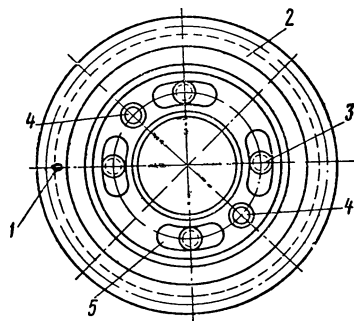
Схема размещения контрольных штифтов, шпилек и контрольной метки на шестерне кулачкового вала топливных насосов: 1 — контрольная метка 0; 2 — шестерня; 3 — шпилька; 4 — отверстия для контрольных штифтов; 5 — паз
